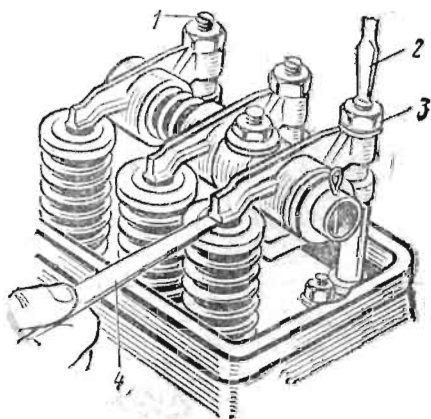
Регулировка зазора между стержнем клапана и носком коромысла двигателя ЗМЗ-24Д, -2401, УАЗ-451, -451М, -451МИ
